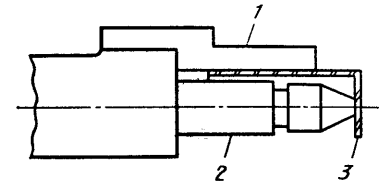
Комбинированный рабочий орган робота (входящее в него зажимное приспособление позволяет исключить операцию подачи деталей). Форма нескольких мелких деталей должна обеспечивать возможность их захватывания одним приспособлением, что позволяет автоматизировать подачу деталей:
